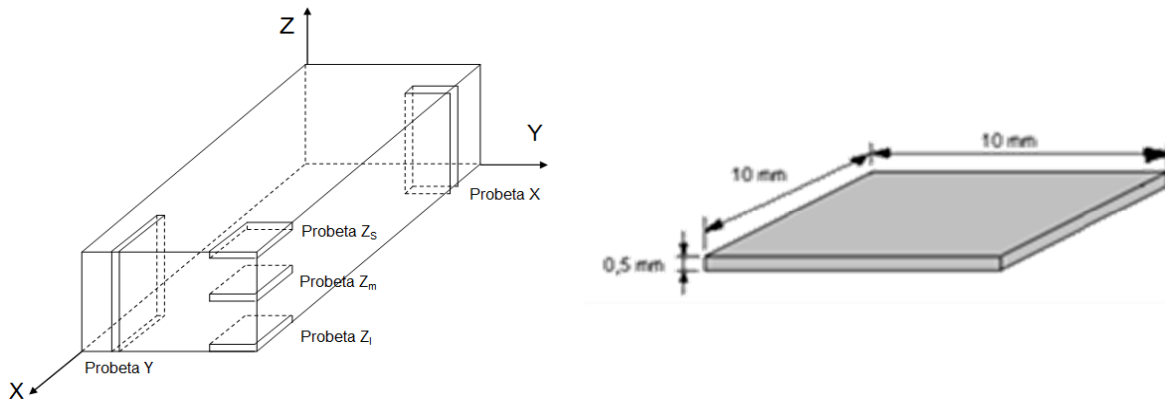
Zonas de extracción, nomenclatura y geometría general de las probetas utilizadas en el ensayo SPT
